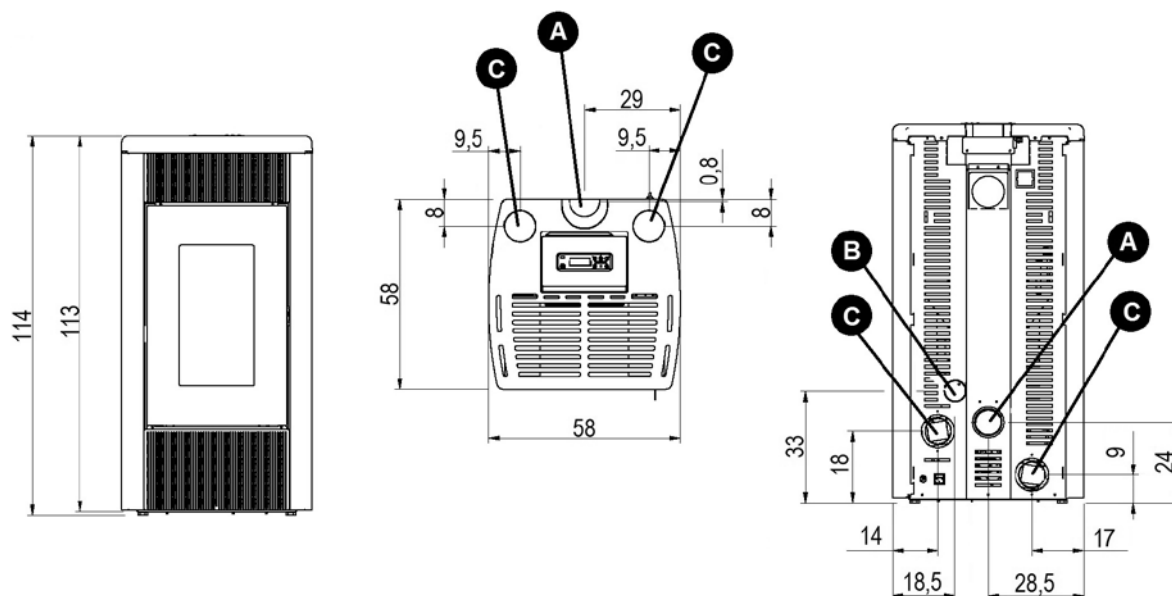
Ogólne wymiary: Duke 12/14 Airtight
